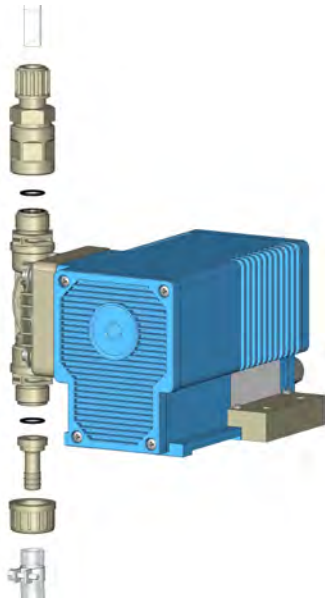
Montage Pumpenanschlusset Turbo Pump
